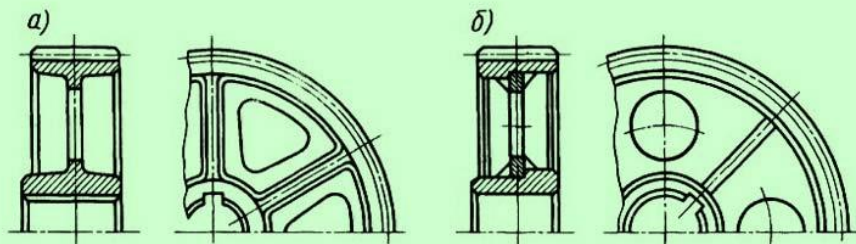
Литые (а) и сварные (б) зубчатые колеса
